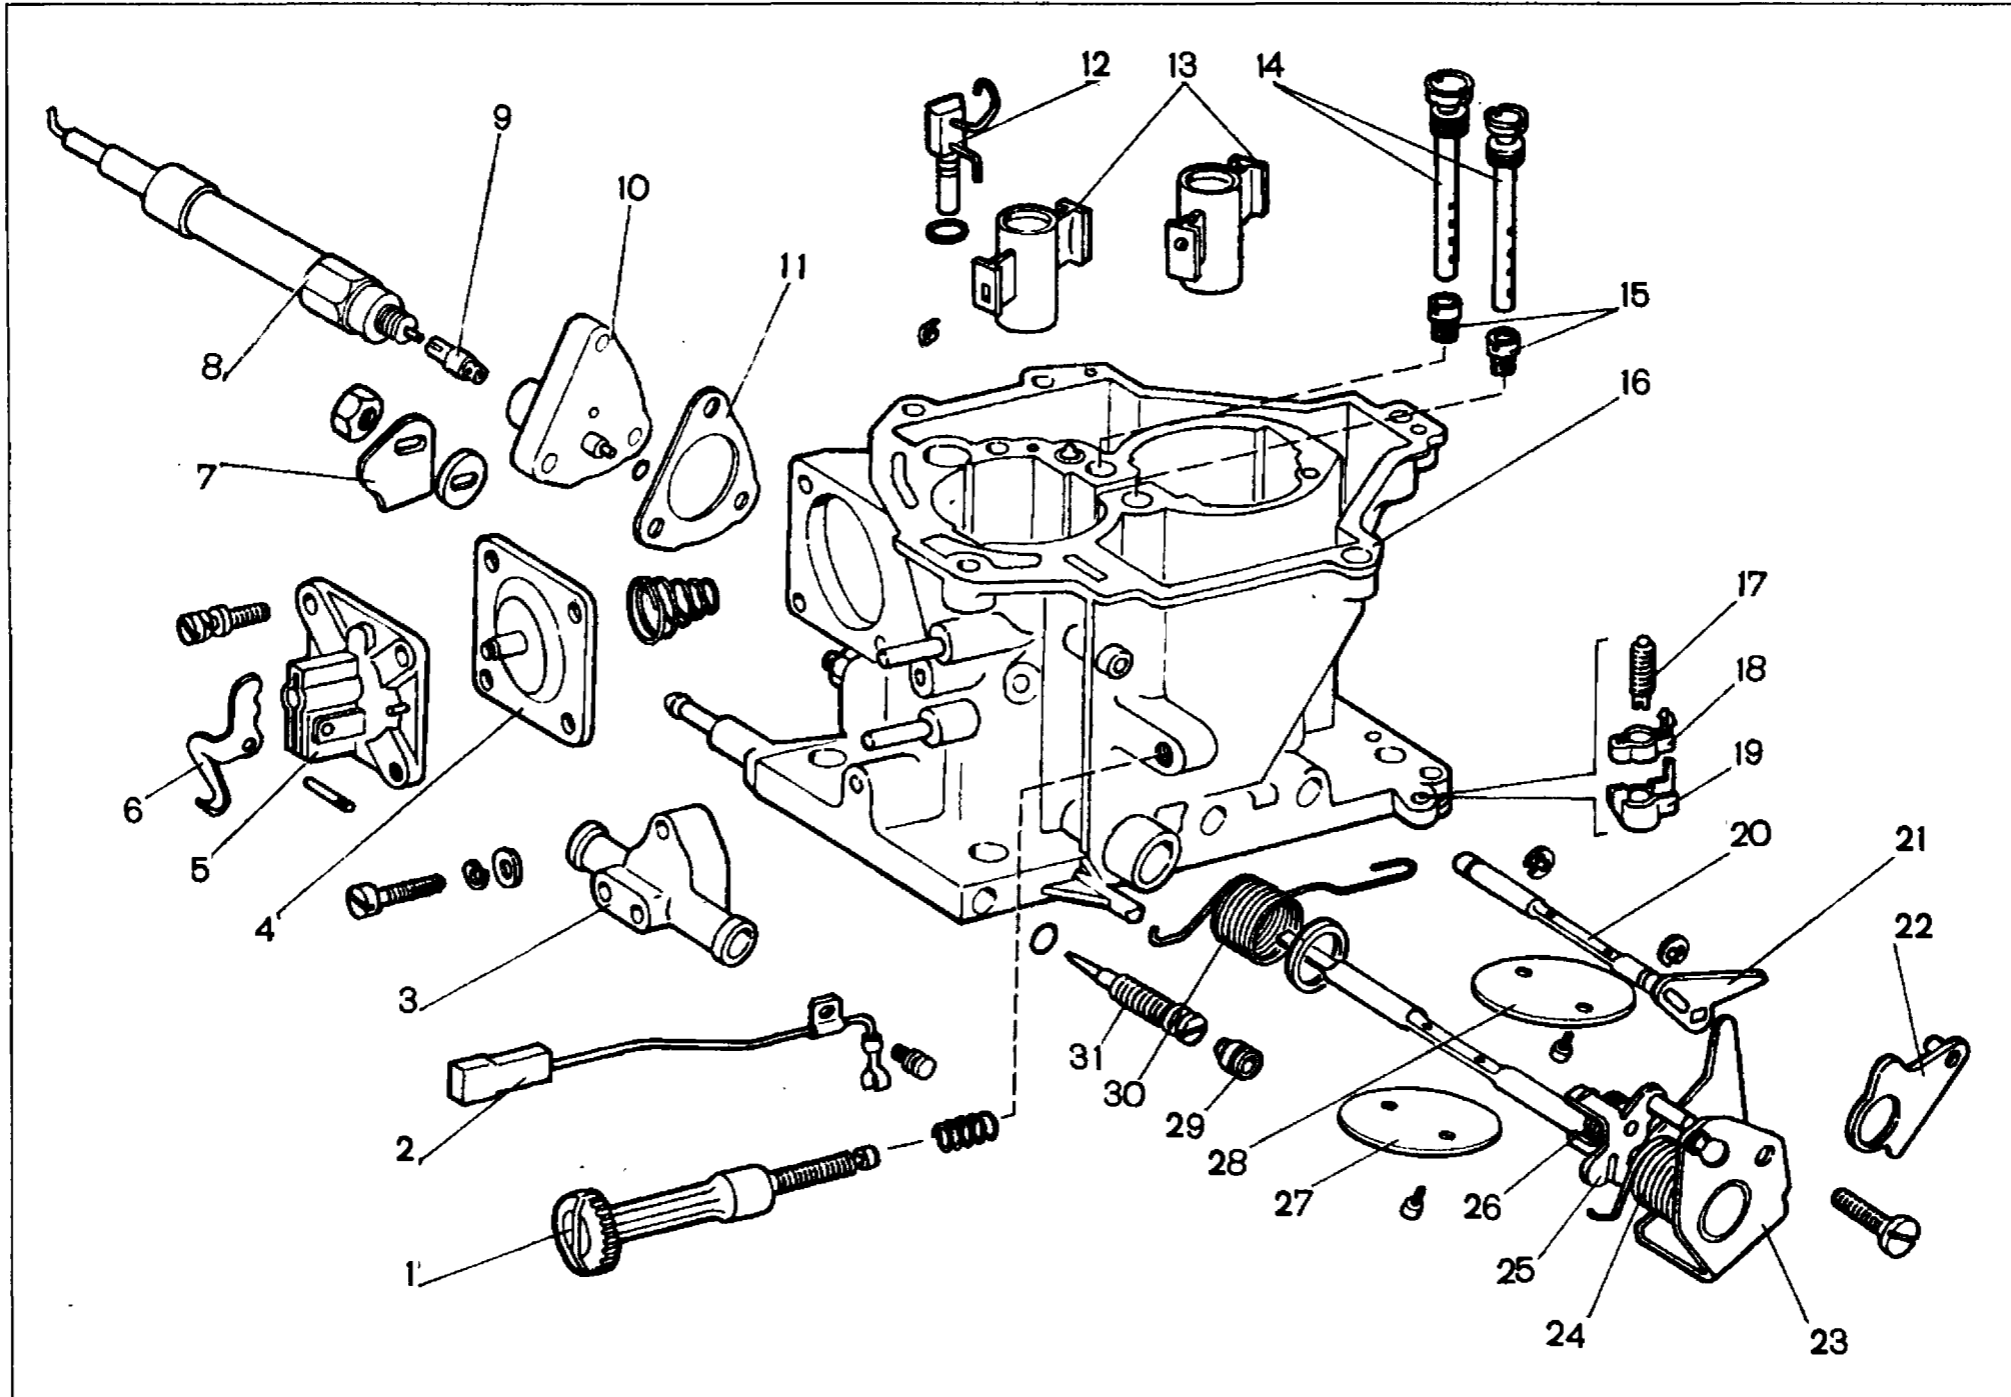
Детали корпуса карбюратора 21083-1107010-62:
